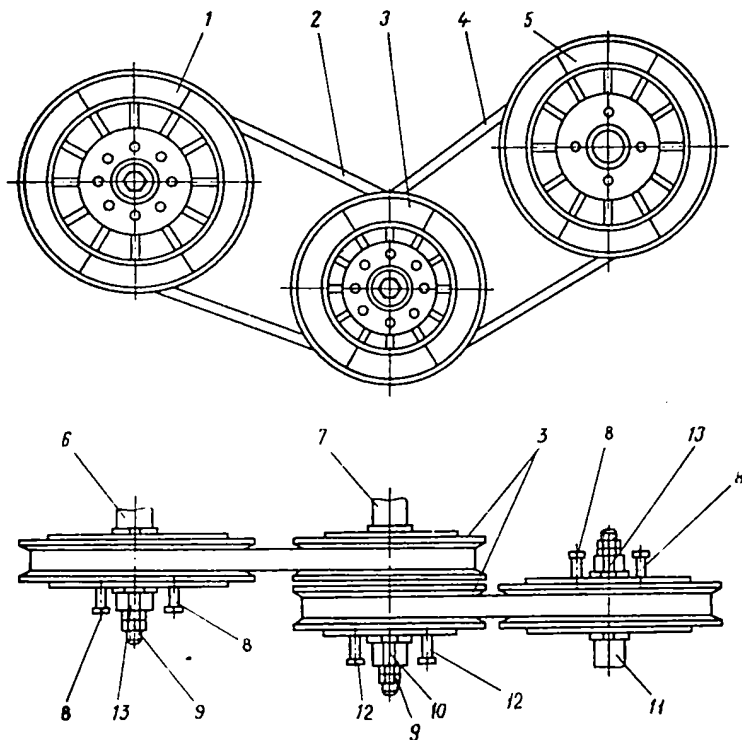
Схема перестановки шкивов барабанов и главного контрпривода: 2,4 – ремни
